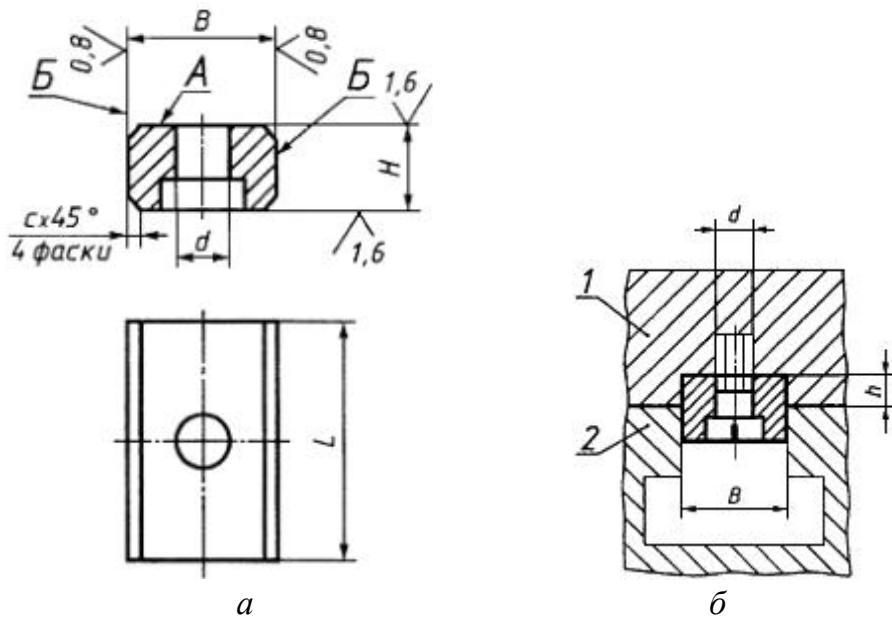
Конструкция (а) и пример применения (б) призматической привертной шпонки, установленной в пазе с резьбой:
